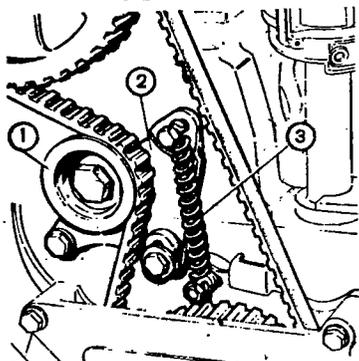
Механизм натяжения ремня привода распределительного вала: 1 - натяжной ролик; 2 - кронштейн натяжного ролика; 3 - натяжная пружина
